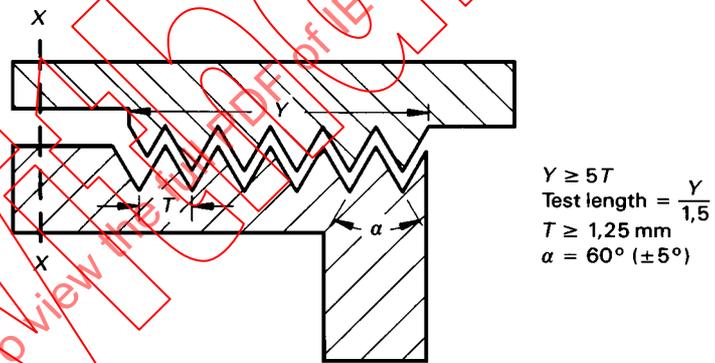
Exemple de joints plans à chicane (voir note 1 de 4.1)
